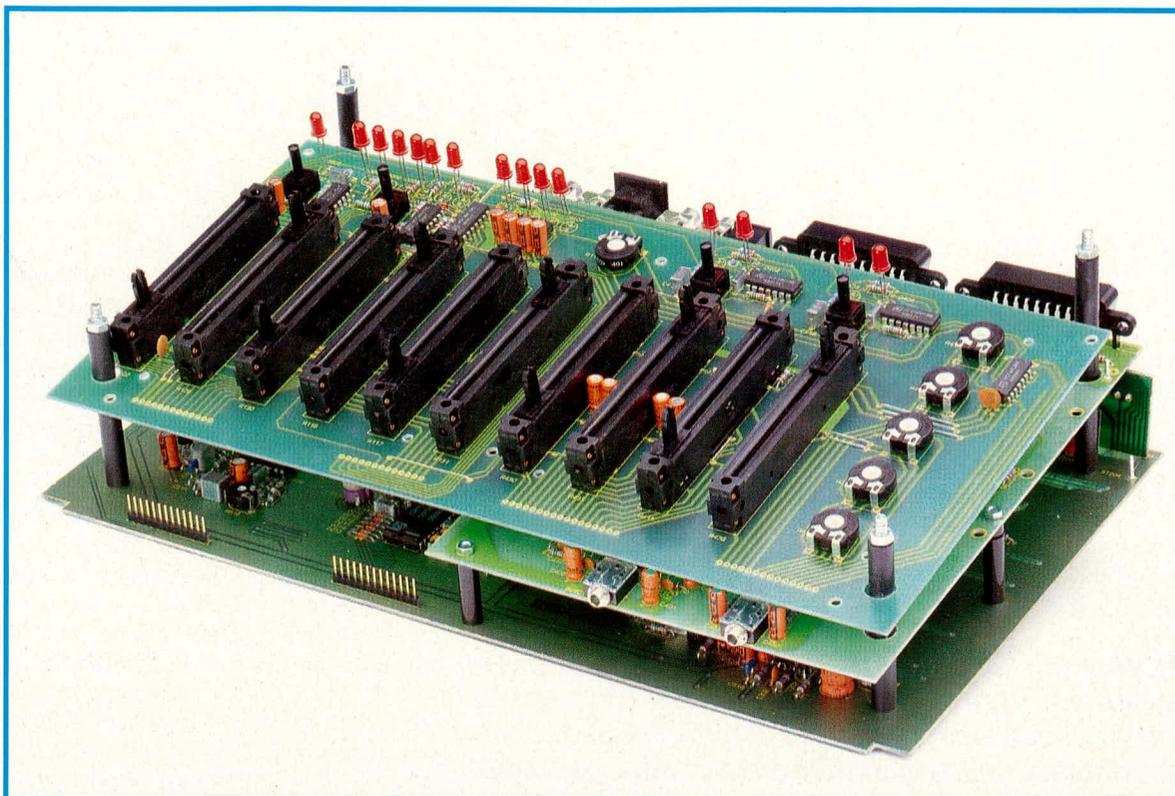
Schematische Anordnung der 4 Einzelplatten, entsprechend der Einbaulage im Gehäuse. Basis-, Zwischen- und Umschalterplatte sind der unteren Halbschale zugeordnet, die Pultplatte dagegen wird über Montage-sockel ins Pultoberteil montiert und bildet ihrerseits das Widerlager für die Befestigungsschrauben der herausnehmbaren Pultplatte.
